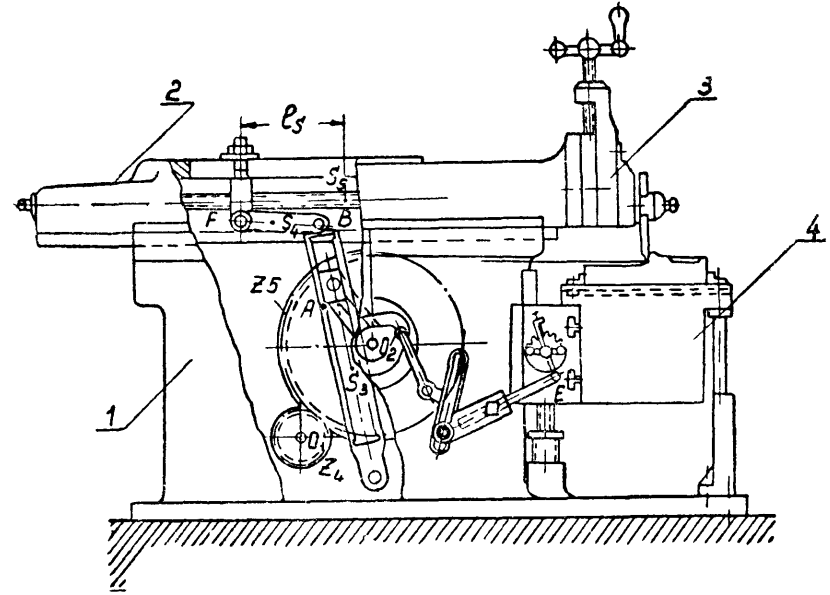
1 Общий вид поперечно-строгального станка с качающейся кулисой
